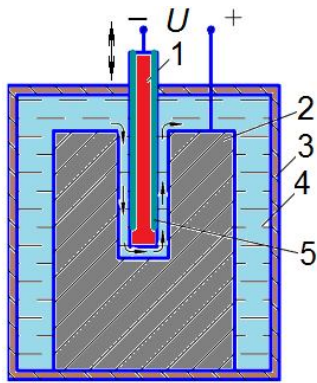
Схема установки для виконання копіювально-прошивних операцій: 1 – електродний інструмент; 2 – заготовка; 3 – камера; 4 – електроліт; 5 – ізоляція
